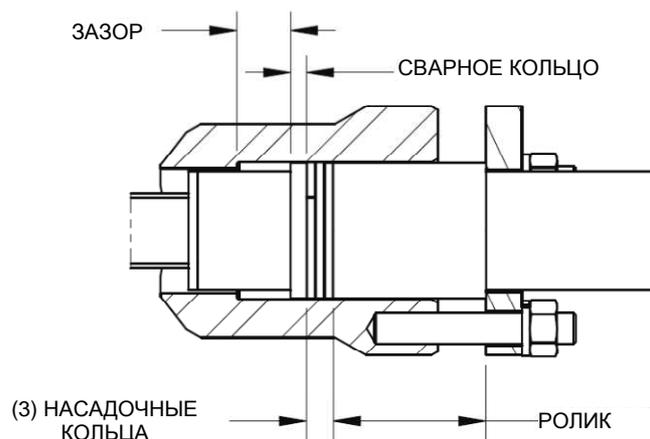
иллюстрирует вид Annubar Pak-Lok по завершении установки. Пожалуйста, обратите внимание, что между корпусом Pak-Lok и сварным кольцом должен быть зазор.
